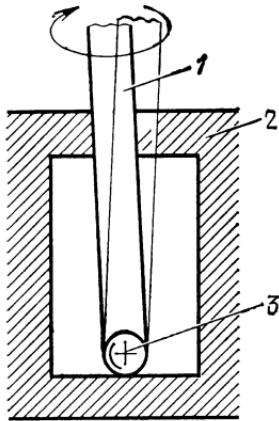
Паразитное движение вала диска проигрывателя в подшипнике:
